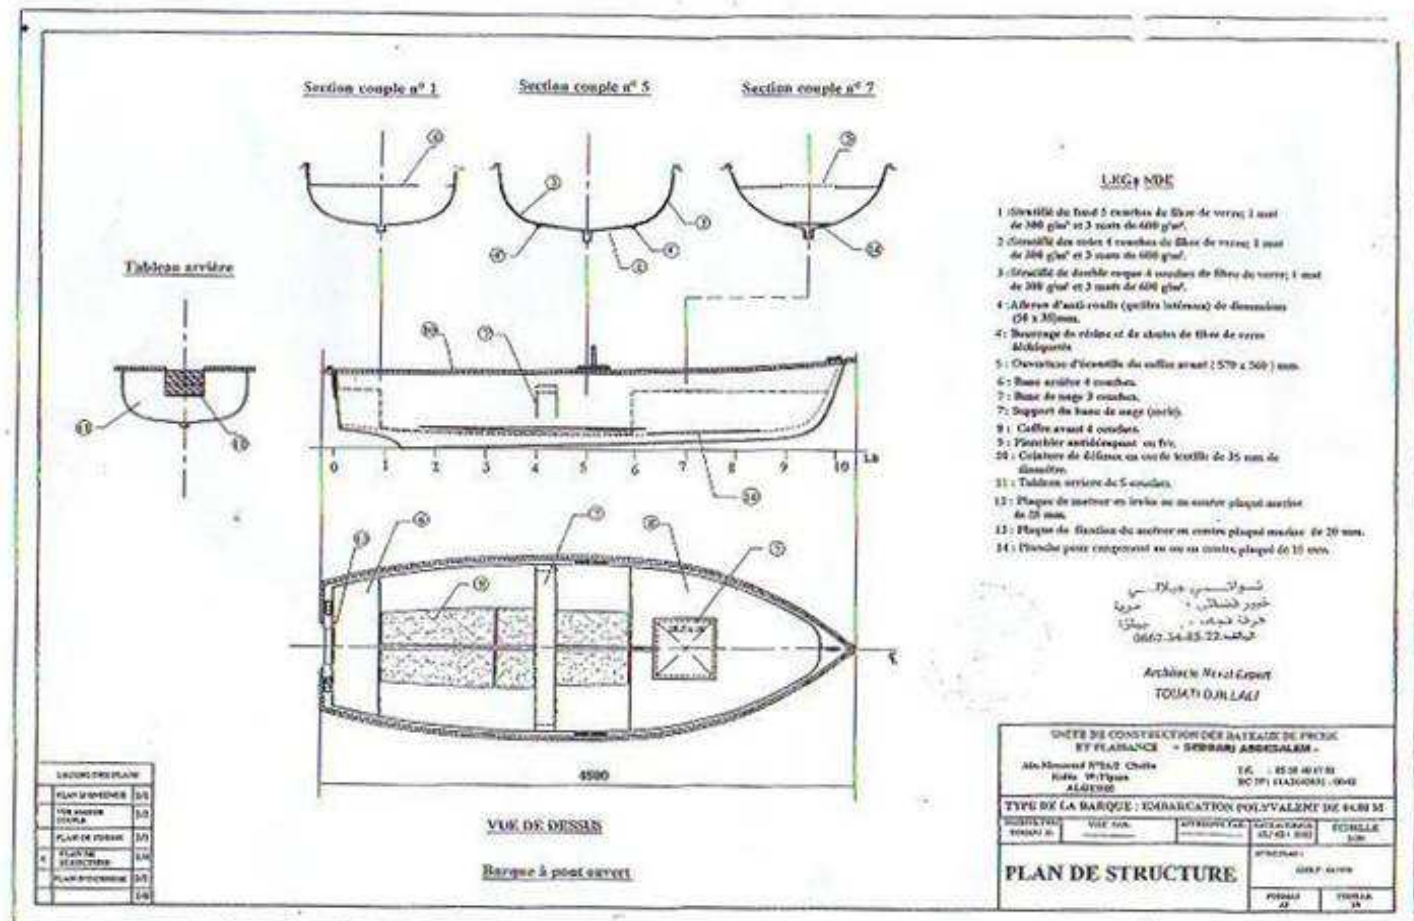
plan de structure et plan d'ensemble d'une embarcation de 4,80 m (plaisancier)
